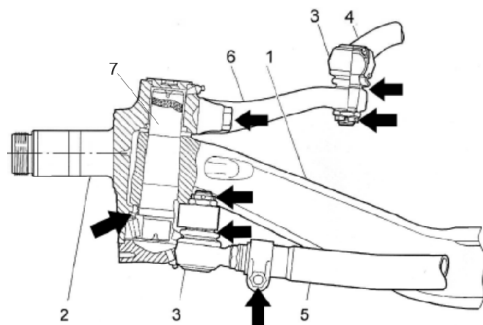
Элементы шкворневой подвески управляемой оси и основные места её контроля: 1 – балка управляемой оси; 2 – поворотная цапфа; 3 – шаровые шарниры рулевых тяг; 4 – продольная рулевая тяга; 5 – поперечная рулевая тяга; 6 – поворотный рычаг; 7 – шкворень.
